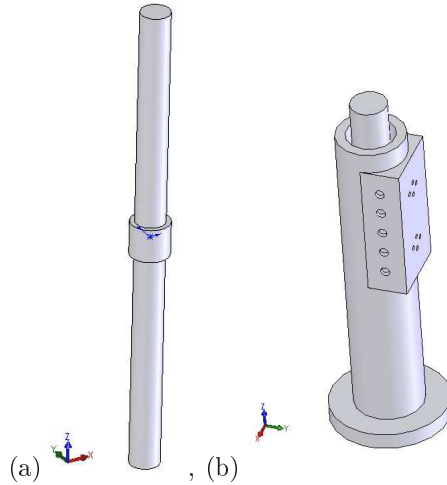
(a) Tige et (b) vérin hydraulique en SolidWorks.
